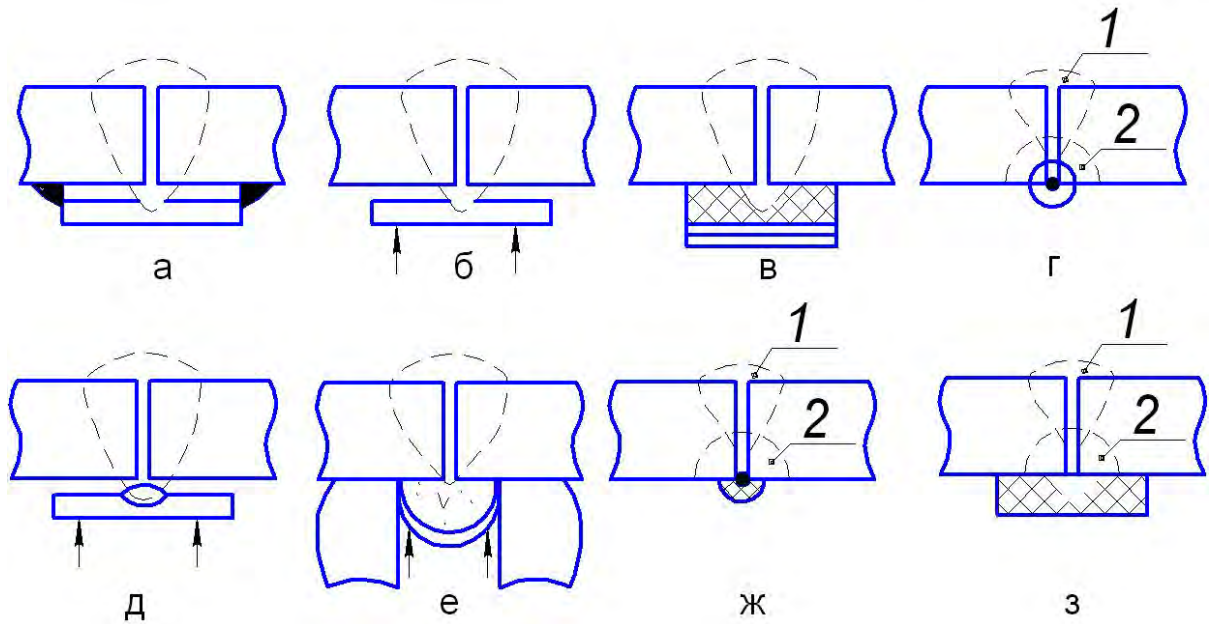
Схемы устройств для удержания сварочной ванны и шлака при сварке под флюсом: а — остающаяся подкладка; б — временная подкладка; в — гибкая лента; г — ручная подварка; д — медно-флюсовая подкладка; е — флюсовая подушка; ж — заделка зазора огнестойким материалом; з — асбестовая подкладка; а, б, в, д, е — односторонний шов; г, ж, з — двусторонний шов; 1 — первый шов; 2 — второй шов
